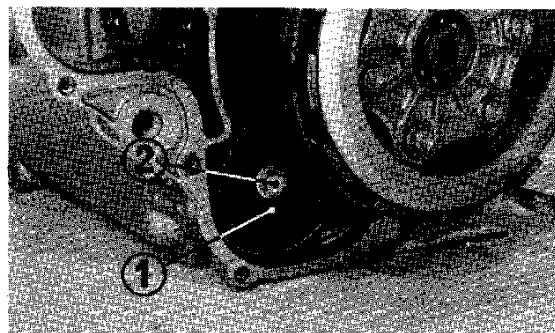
(1) Ölpumpen-Antriebskettenrad
